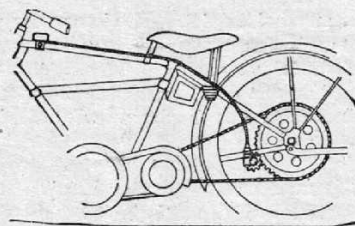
Kettenmaschine mit Spezialantrieb vom Hinterrad aus.
